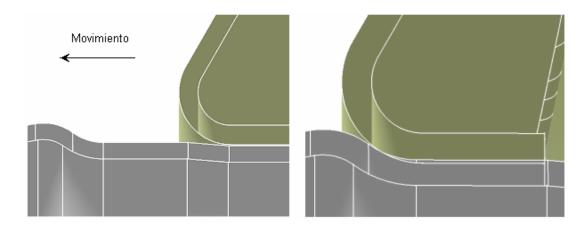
Proceso de inserción. Posición inicial y final.
